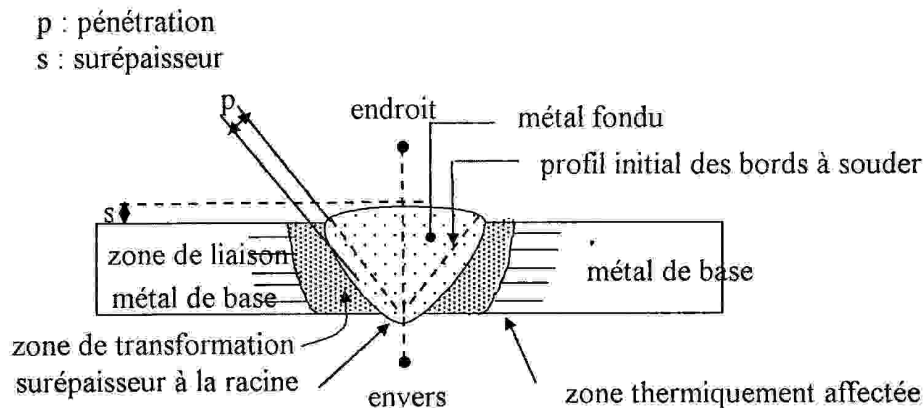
Soudure (bout à bout sur chanfrein en V) [3]
